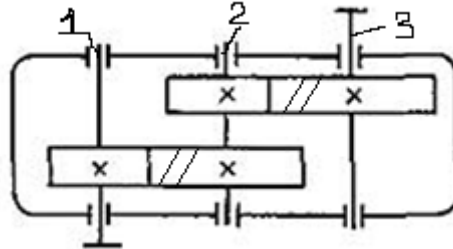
Схема двухступенчатого редуктора с цилиндрическими косозубыми передачами
